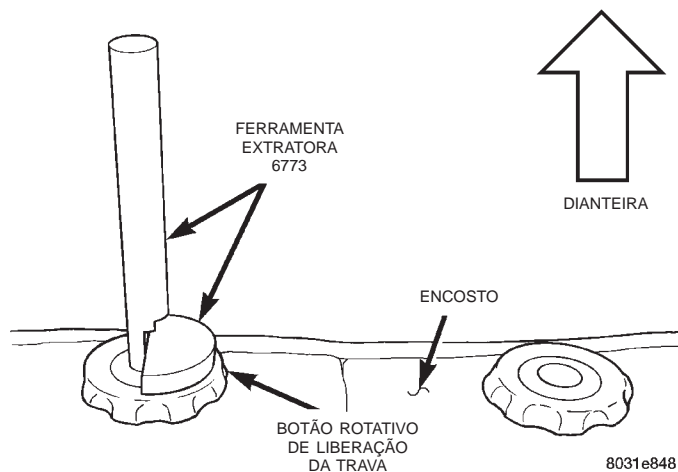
Posicionamento do Extrator da Bucha de Apoio de Cabeça
